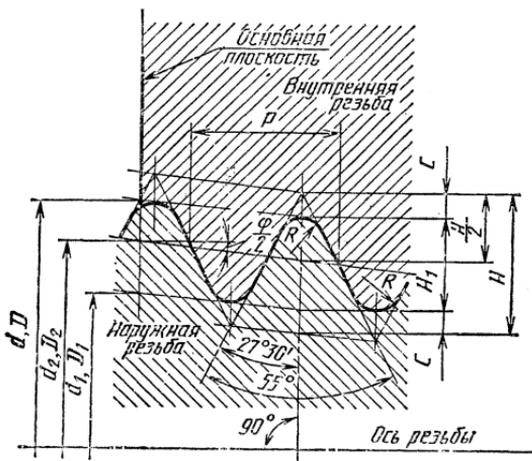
Основные элементы трубной конической резьбы (ГОСТ 6211—81):
